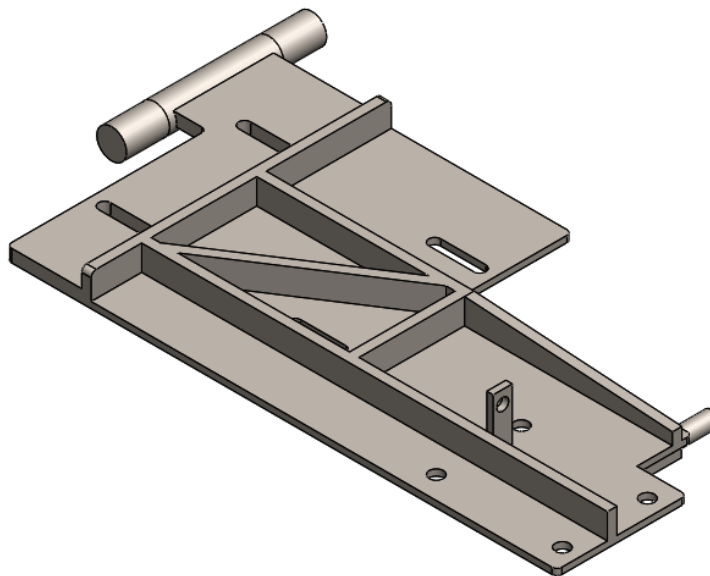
Chapa portante de motor, sistema de transmisión y sierra
